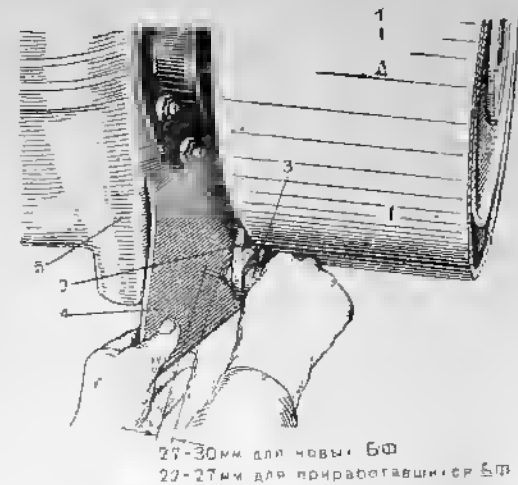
Проверка зазора в шариках механизма выключения бортового фрикциона: 1 — бортовой фрикцион; 2 — рычаг подвижной чашки; 3 — керн; 4 — дощечка; 5 — картер коробки передач
